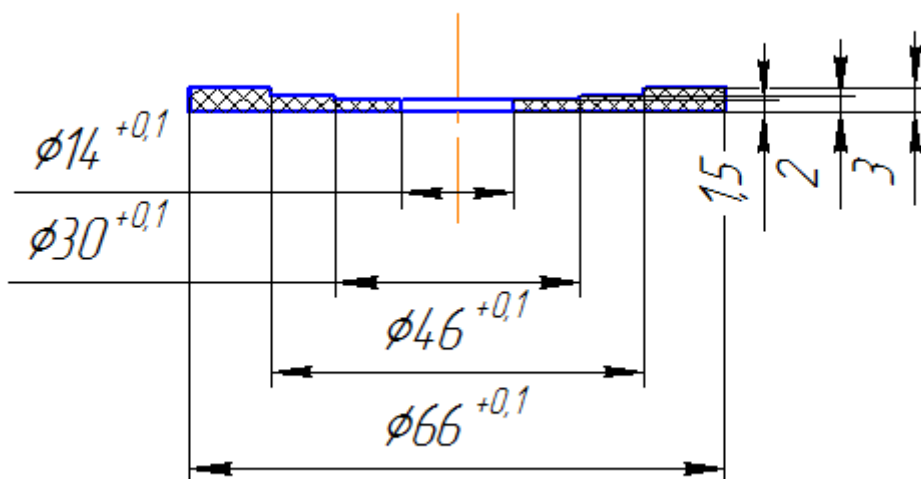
Конструкція дискового перетворювача ступінчатої форми
